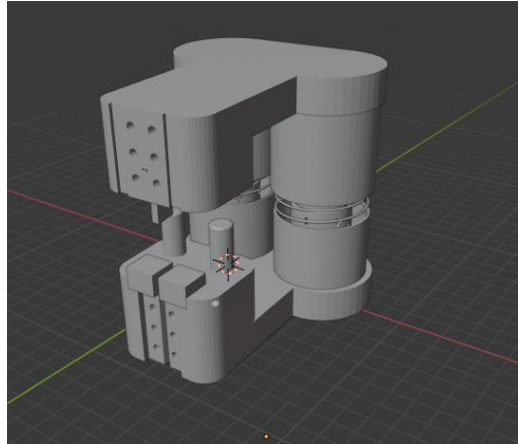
Ensamble troquel de corte punta importado sin modificar en Blender
